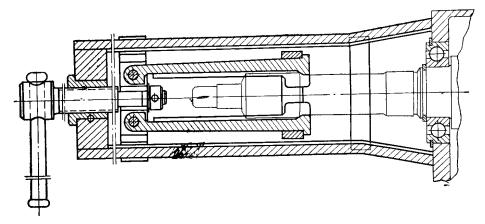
Съемник ведущего вала с подшипником из картера коробки передач
